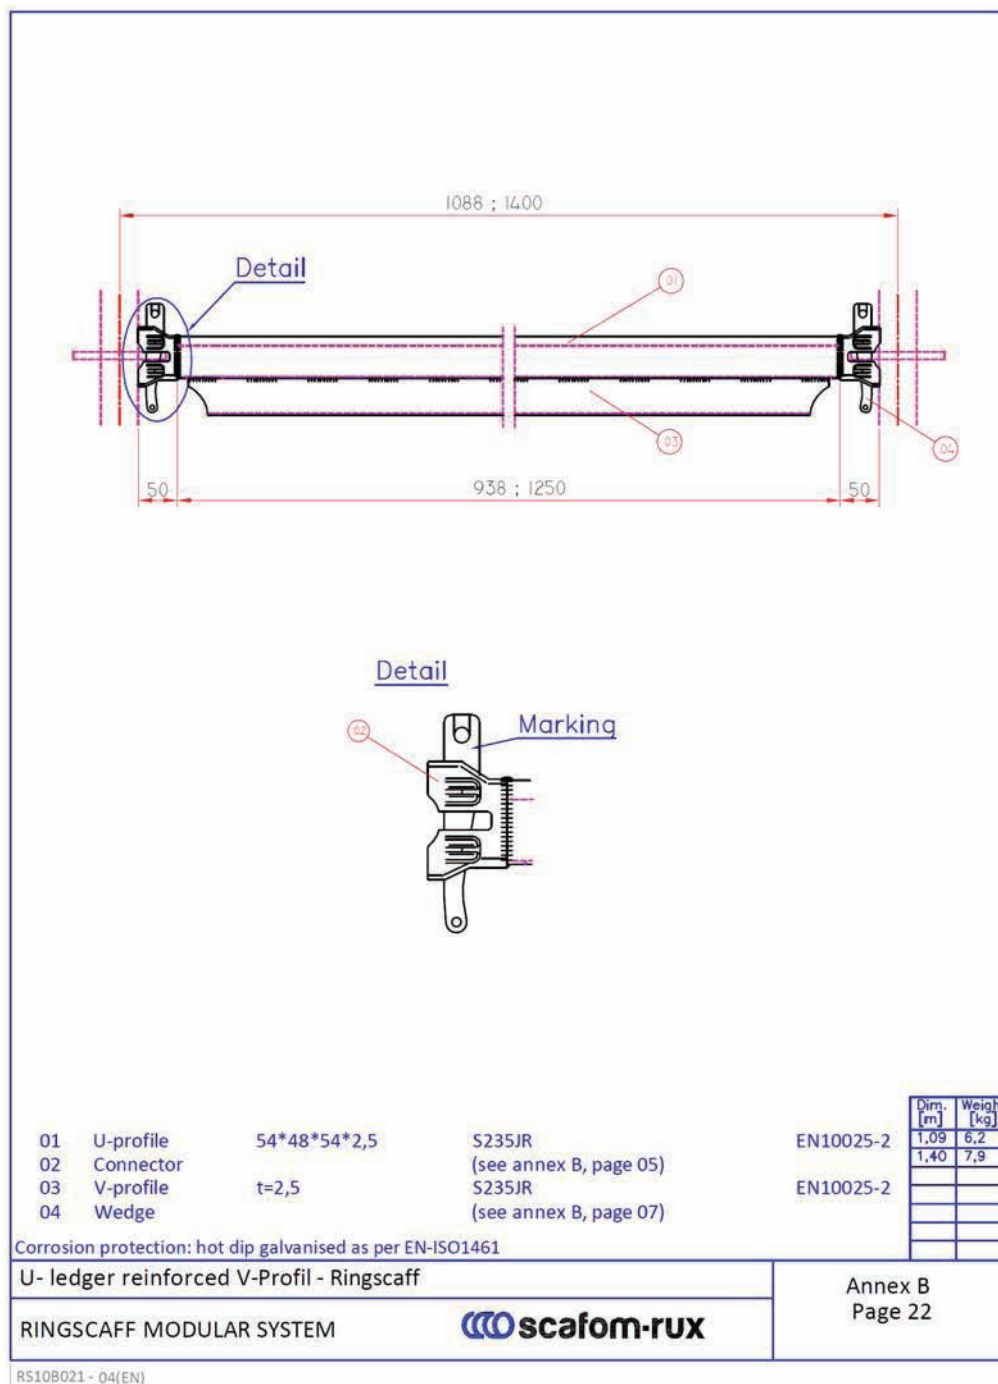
Travessa com secção em U reforçada com perfil em V
